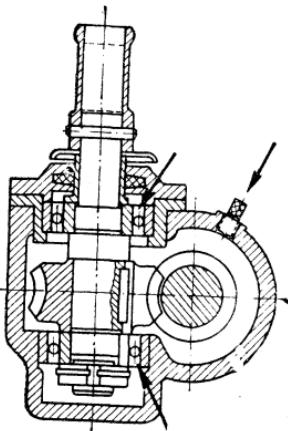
Смазка якорных подшипников мотор-вентилятора НБ-430А
